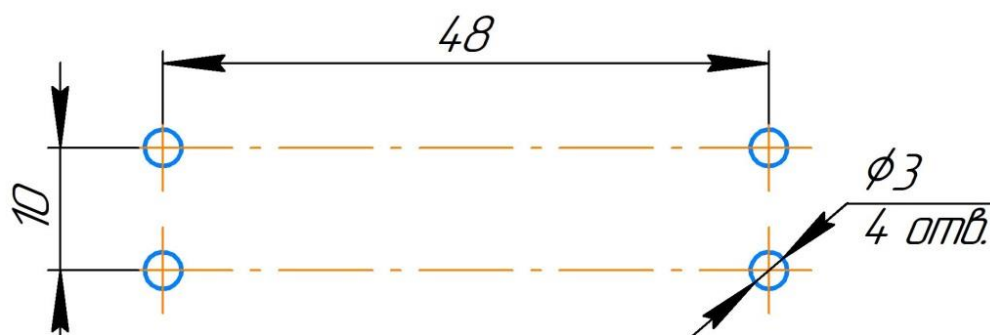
Схема отверстий для крепления сервопривода
